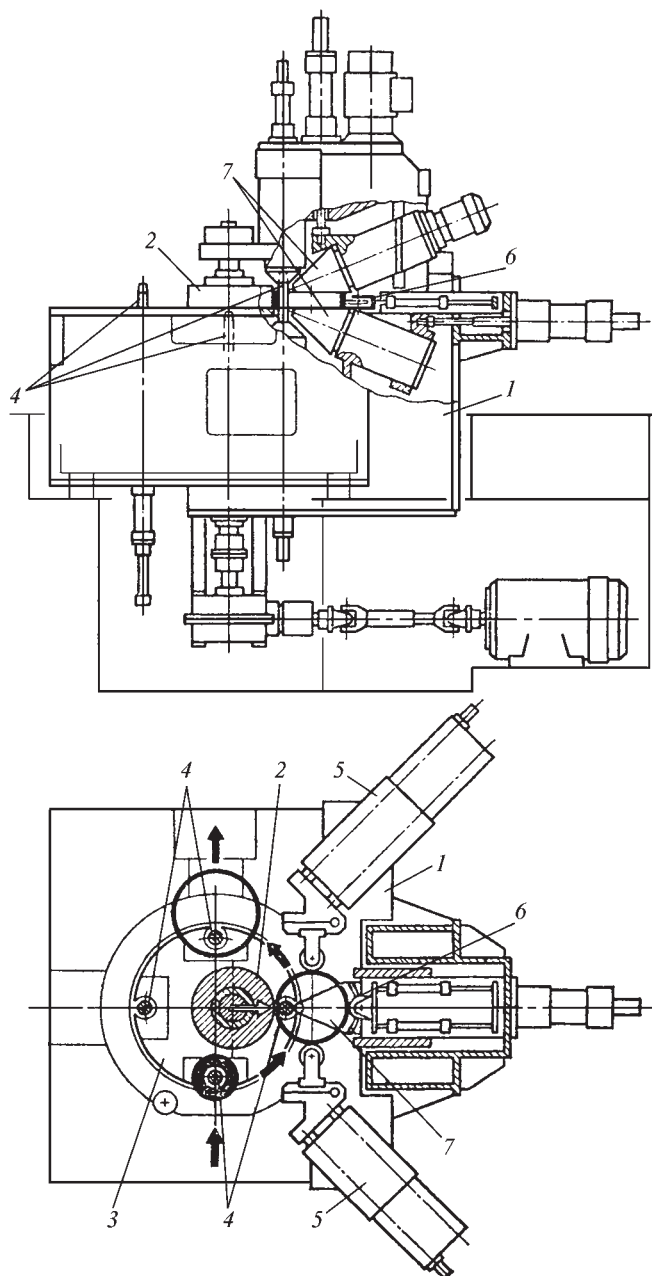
Компонировочная схема кольцеракатного автомата типа КФРАВМ:
